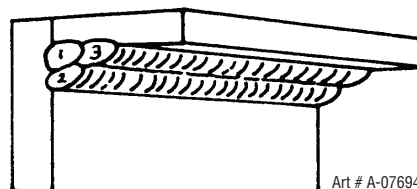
Position au plafond, soudure d'angle
